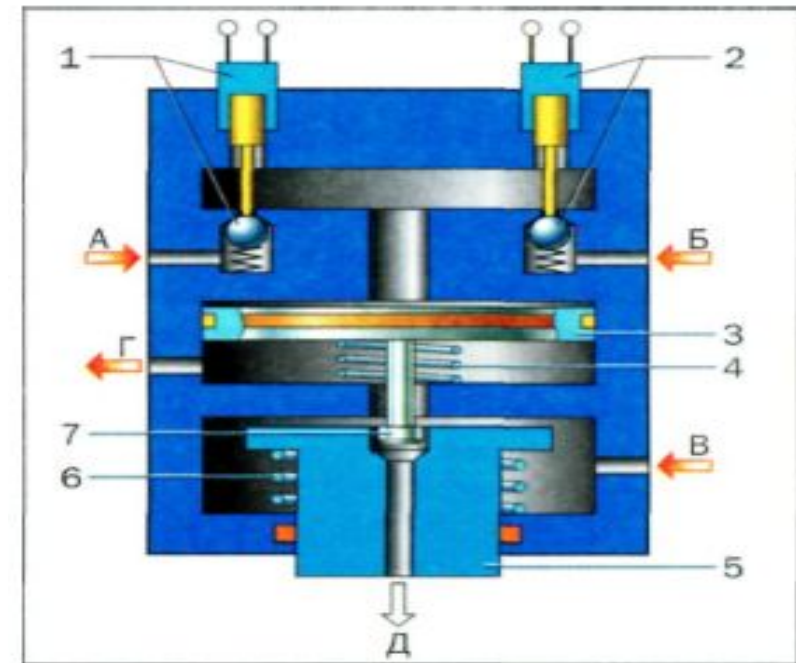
Принципиальная схема пневматического модулятора АБС: 1, 2 — электромагнитные клапаны; 3 — следящий поршень; 4, 6 — пружина; 5 — корпус впускного и атмосферного клапанов; 7 — седло атмосферного клапана; А — полость, соединяющая тормозной кран с модулятором; Б — полость, соединяющая модулятор с атмосферой; В — полость, соединяющая воздушный баллон с модулятором; Г — полость, соединяющая модулятор с рабочей полостью тормозной камеры; Д — полость, соединяющая тормозную камеру через модулятор с атмосферой
